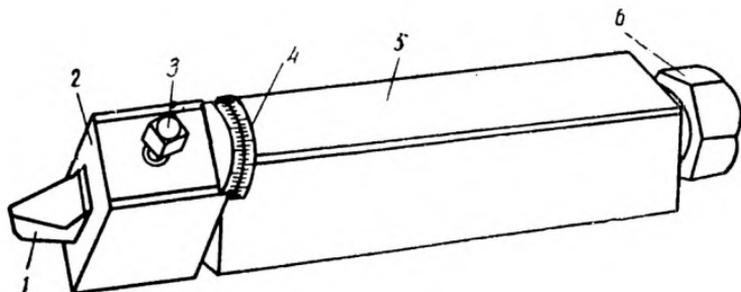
Установка резьбового резца по углу подъема винтовой линии.
